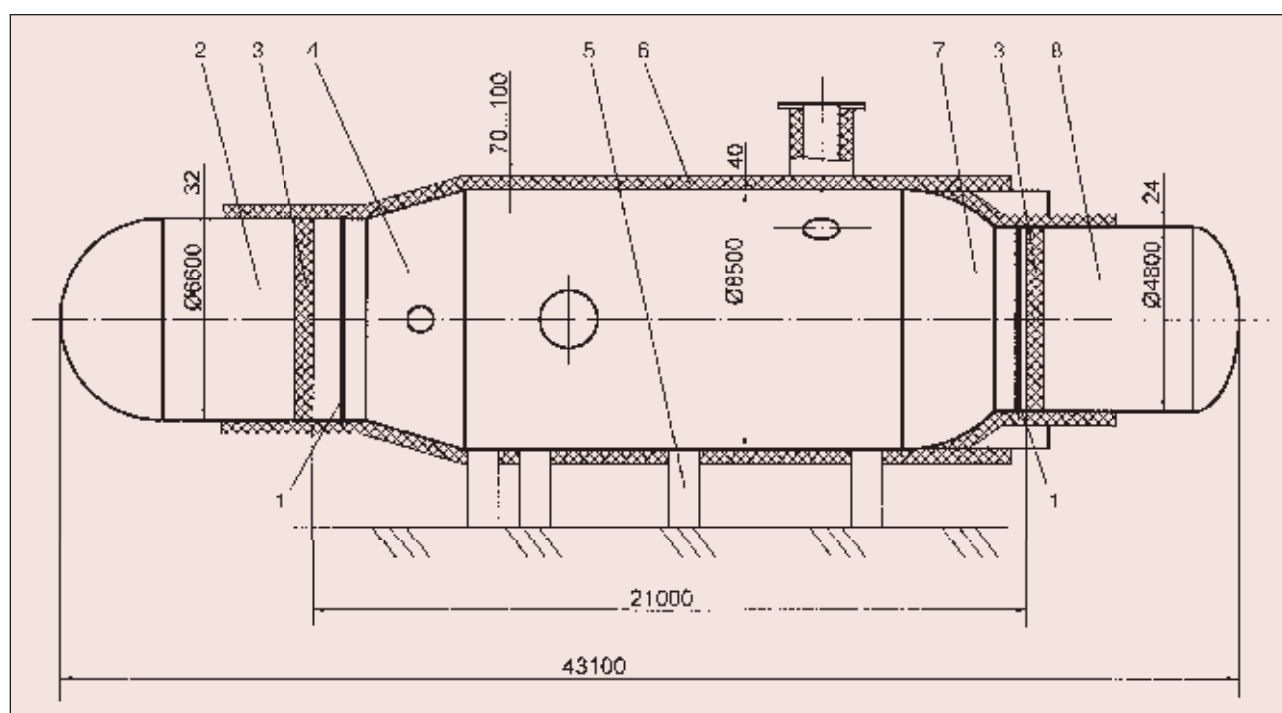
Схема расположения колонны и установки теплоизоляции: 1 — замыкающий сварной шов; 2, 7, 8 — основные сборочные элементы; 3 — теплоизоляционные перегородки; 4 — корпус; 5 — опоры; 6 — наружная теплоизоляция
